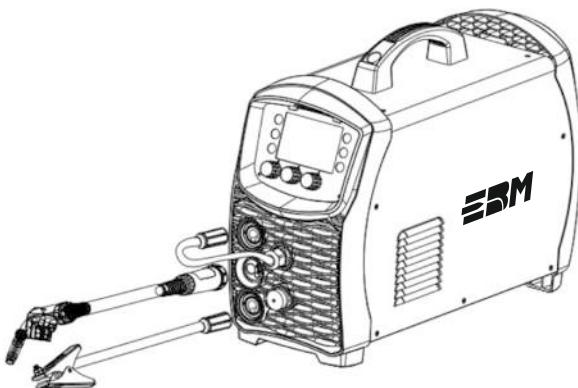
Схема подключения кабелей для сварки самозащитной порошковой проволокой
